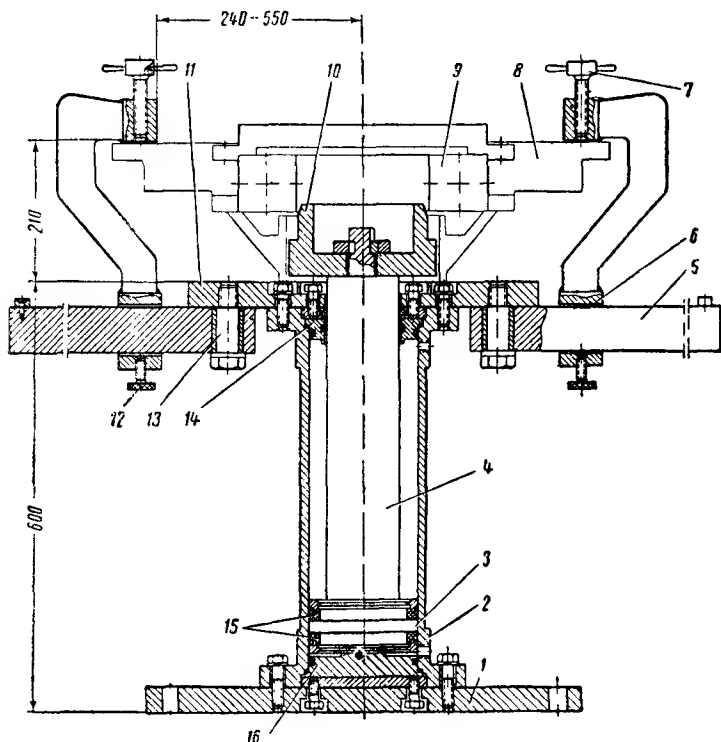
Гидравлический пресс для выпрессовки роликовых подшипников из щитов тяговых двигателей:
